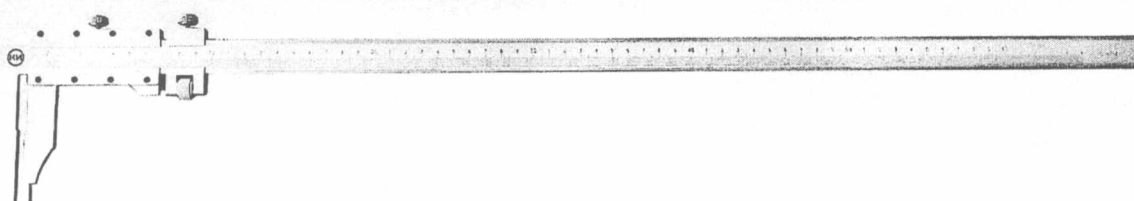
Общий вид штангенциркулей типа ШЦ-III
